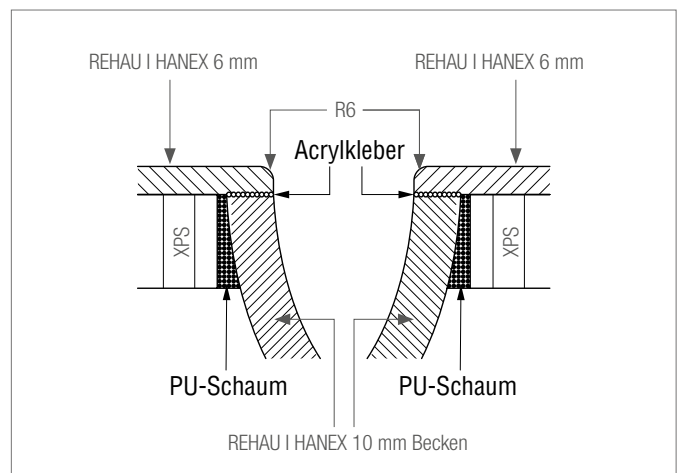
Ausschnittkante bündig fräsen und mit Radius versehen
